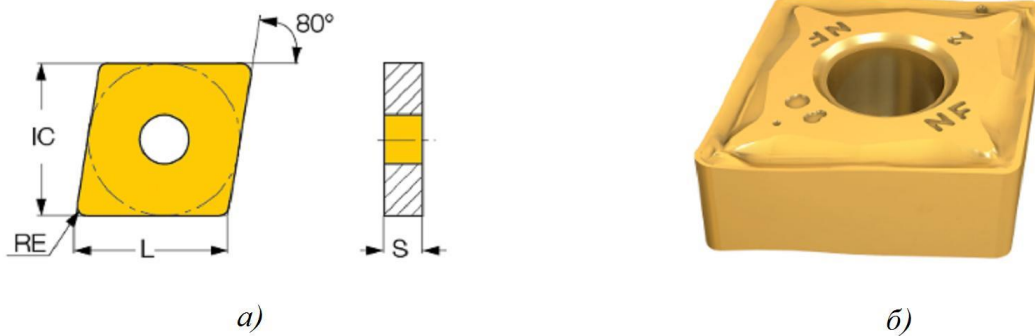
Пластина проходная [1]: а- схема; б - общий вид
